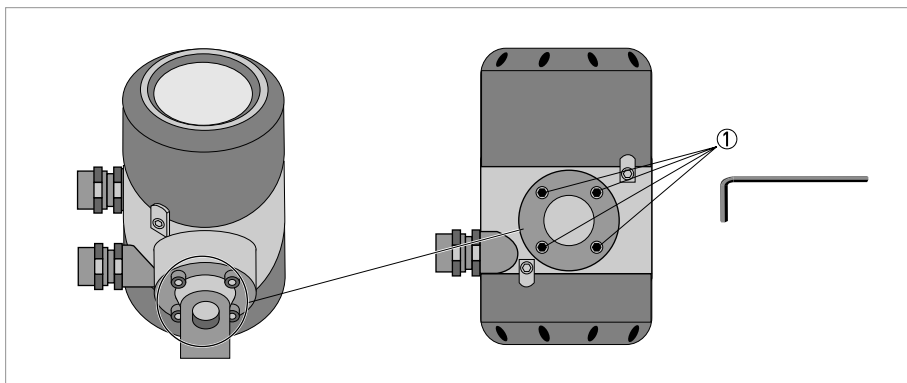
Innensechskantschrauben am Anschlussgehäuse
